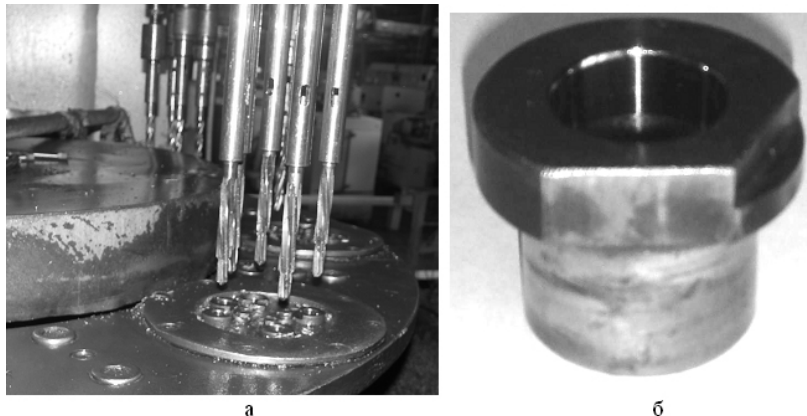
Многошпиндельный сверлильный станок с кондукторными втулками
